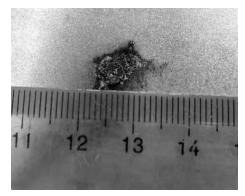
侧围上边梁内侧焊渣形貌 Fig.3 Morphology of welding slag inside the rood side rail of side wall
